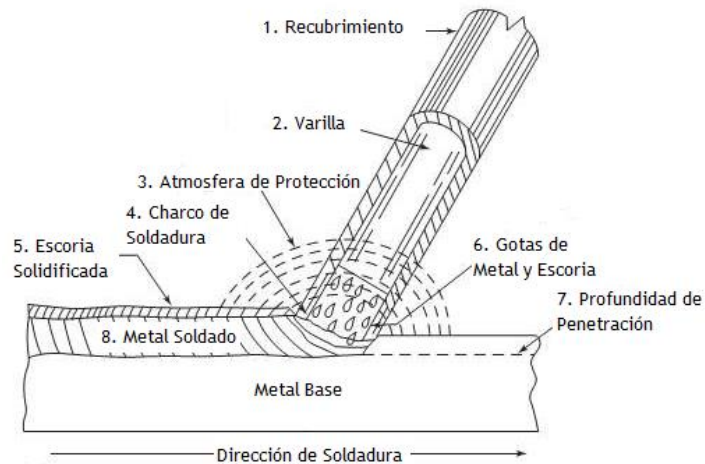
Partes del Proceso Shielded Metal Arc Welding (SMAW).
